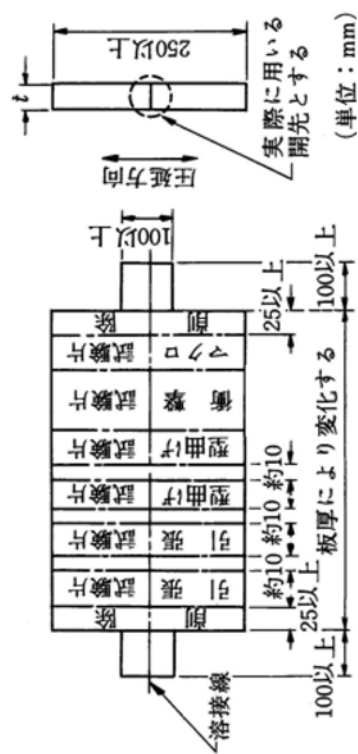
衝撃試験片（開先溶接試験片の採取位置）
